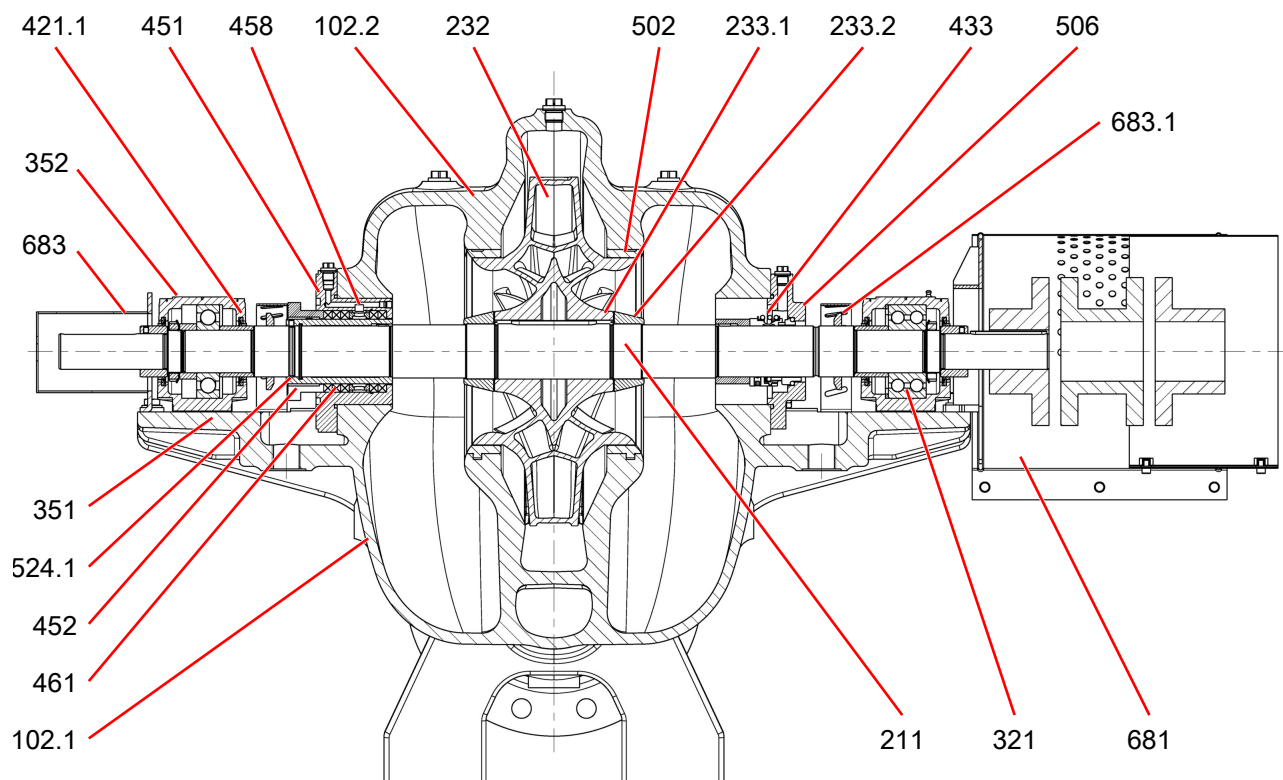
Чертеж насоса ASP-R в разрезе (соосные лопасти рабочего колеса, призматическая шпонка)
